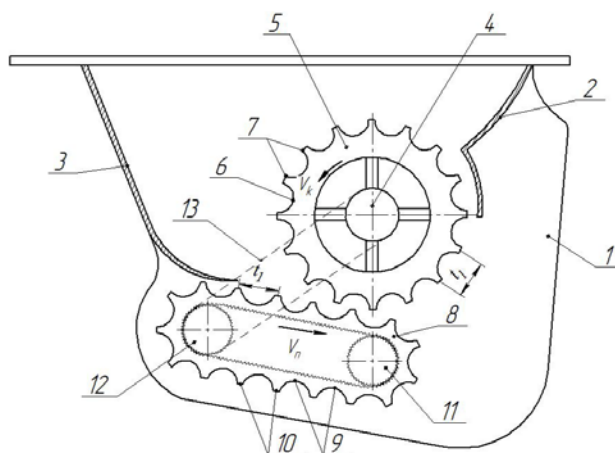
Конструктивна схема катушкового висівного апарата: 1 – боковини; 2, 3 – передня і задня стінки; 4 – приводний вал; 5 – висівна катушка; 6, 9 – жолобки; 7, 10 – виступи; 8 – клапан; 11, 12 – вали; 13 – передача.
